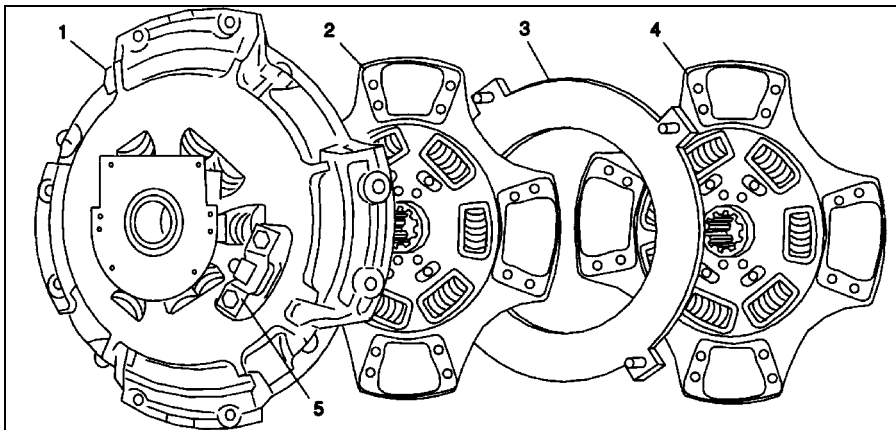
Сцепление Easy-Pedal. 1 - корзина сцепления, 2 - задний ведомый диск, 3 - промежуточный диск, 4 - передний ведомый диск, 5 - механизм регулировки.
